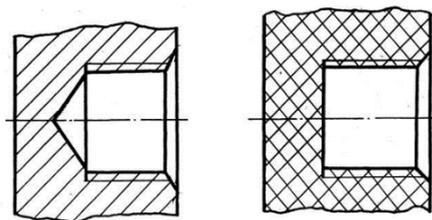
Изображение конца глухого резьбового отверстия на чертежах (сборочных, общего вида и др.), по которым резьба не выполняется
